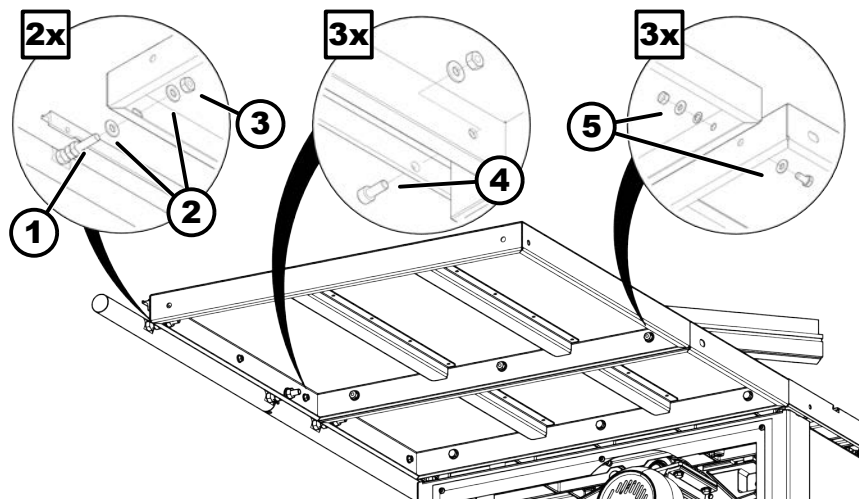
Montage de l'élargissement de coupe - variante 1220
